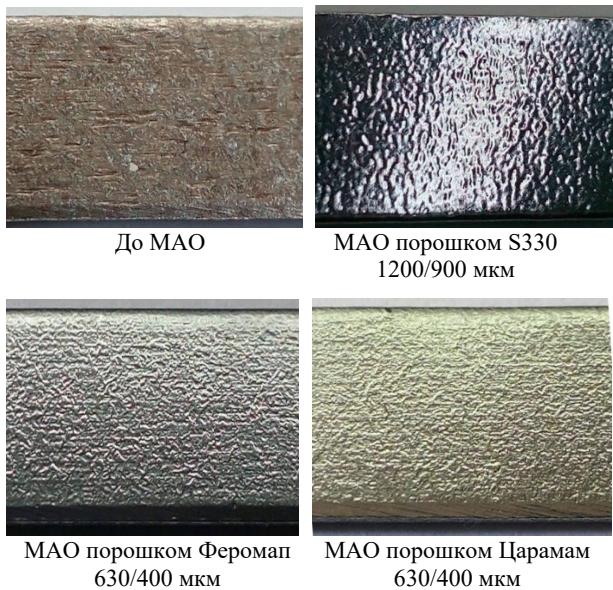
Зовнішній вигляд поверхонь зразків після оброблення
